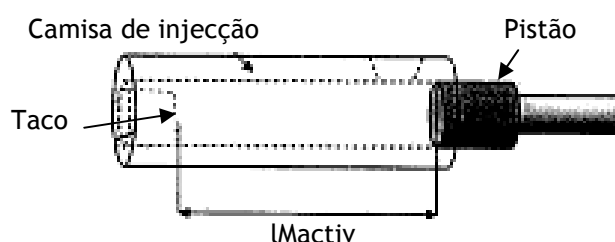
Comprimento útil da camisa de injeção para o molde com taco [10]
